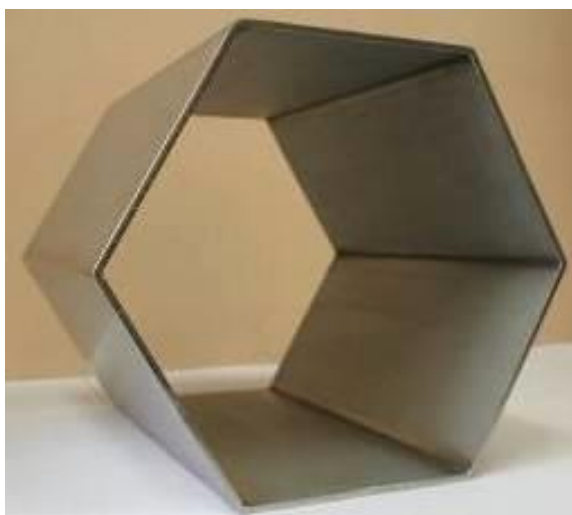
Образец трубы, изготовленной с помощью ЭЛС
